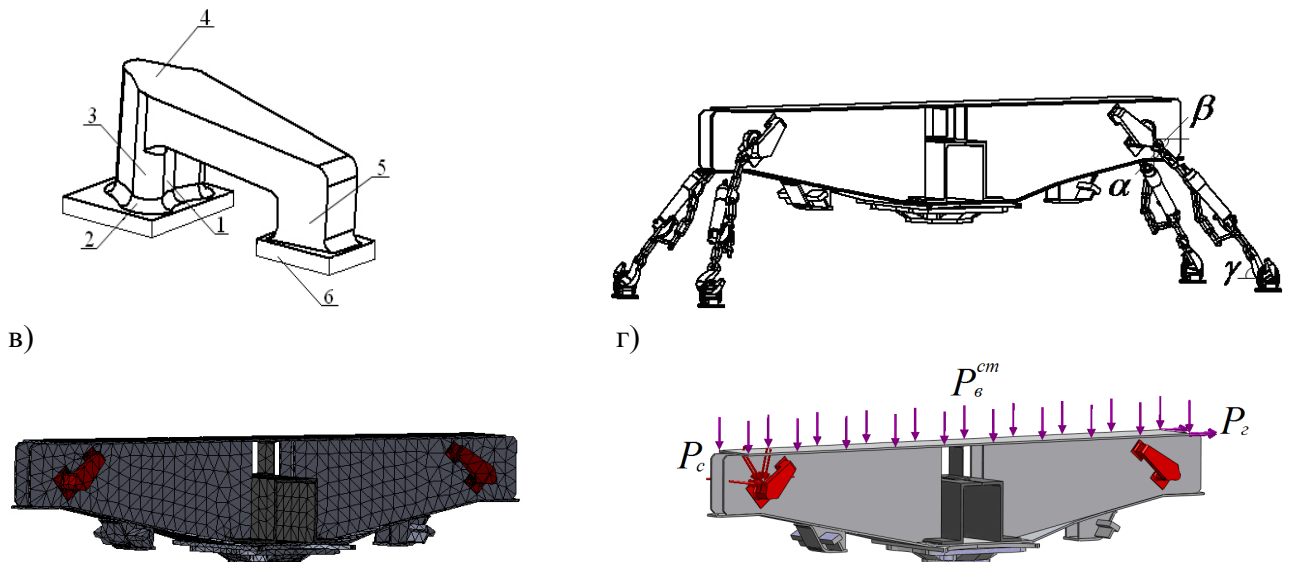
Вузол для закріплення гака ланцюгової стяжки:
